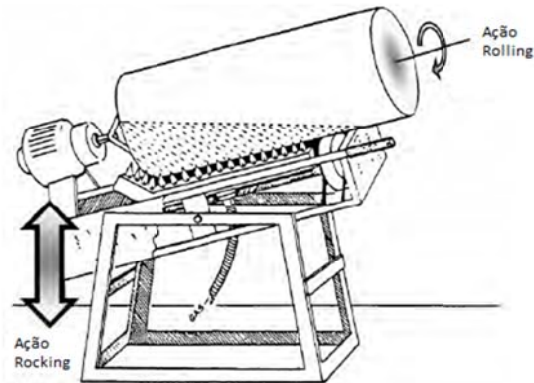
Máquina de rotomoldagem do tipo *rock-and-roll*.
